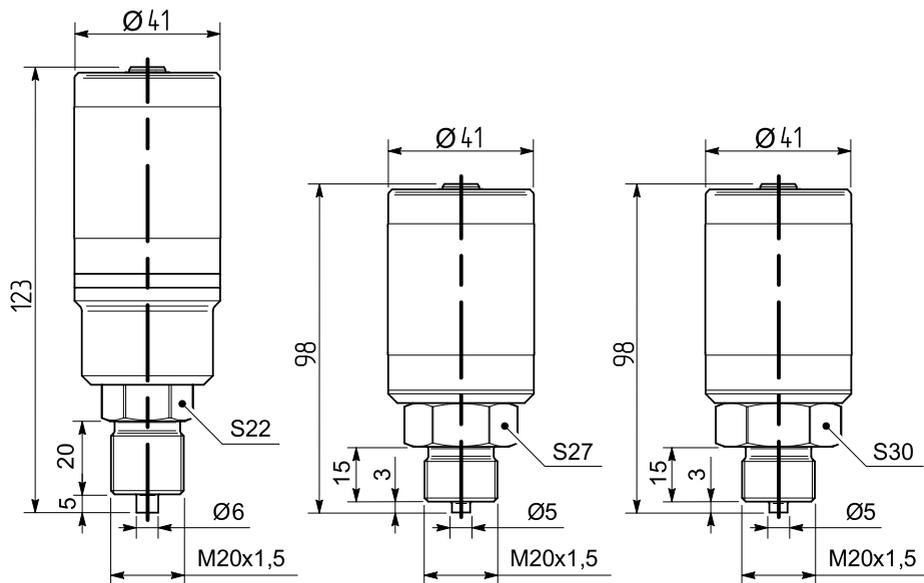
Габаритные размеры преобразователей исполнений 1 и 2.
